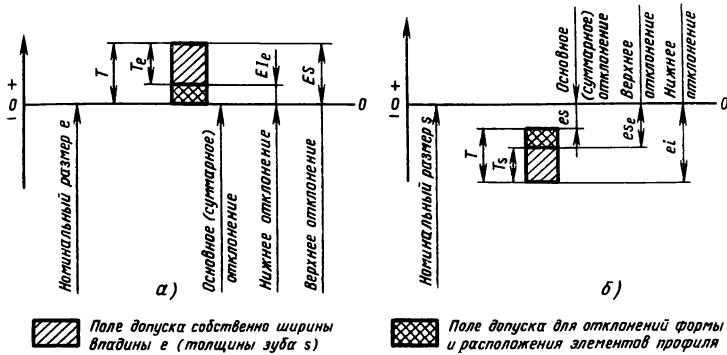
Расположение полей допусков ширины впадины e втулки (*a*) и толщины зуба s вала (*b*)
